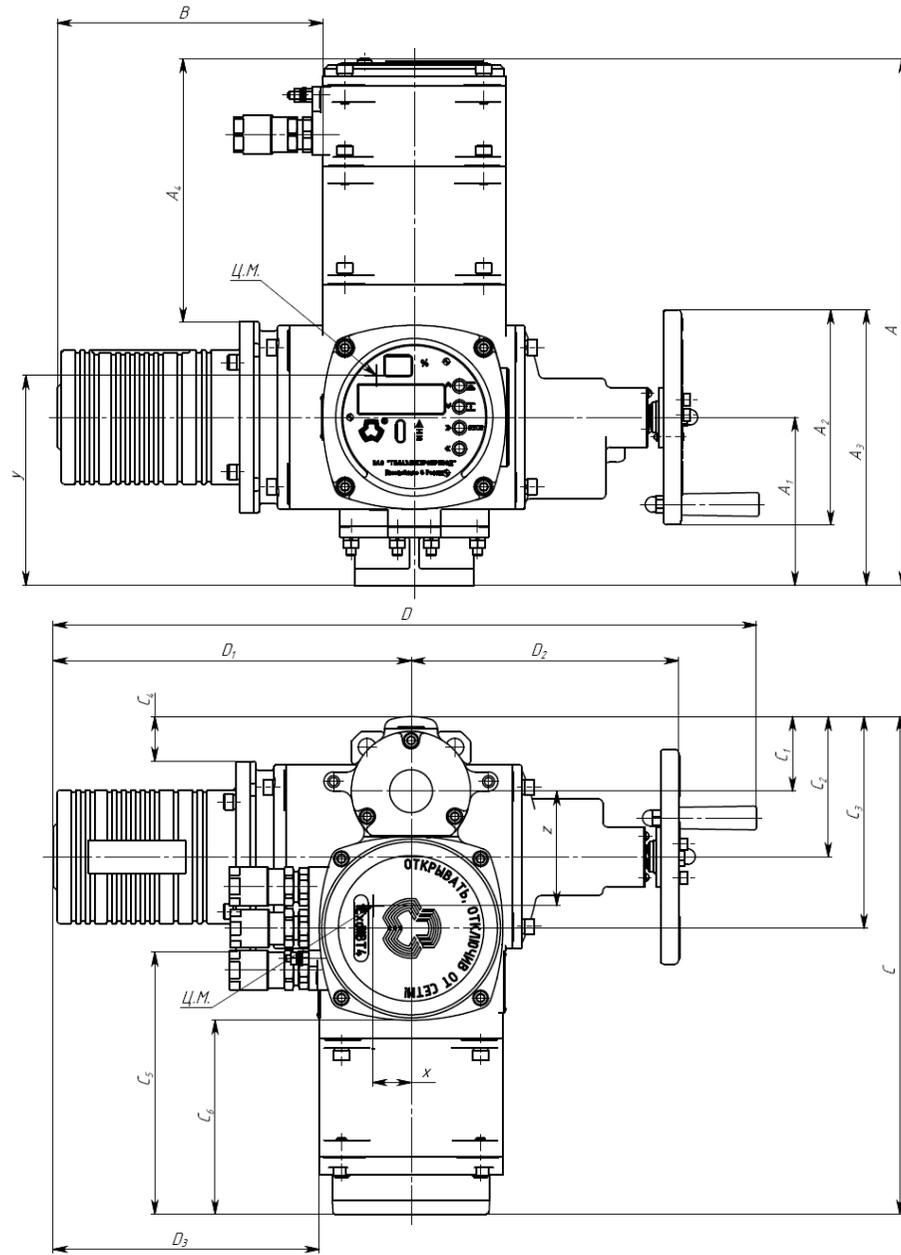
а – Габаритные размеры привода конструктивной схемы 40
